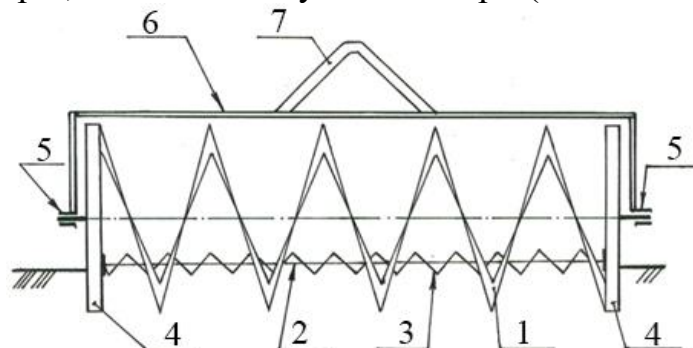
Схема ґрунтообробного знаряддя: 1 – спірально-гвинтовий робочий орган; 2 – вал шнека; 3 – шнек; 4 – механізм приводу робочих органів; 5 – підшипники; 6 – рама; 7 – механізм навішування.
